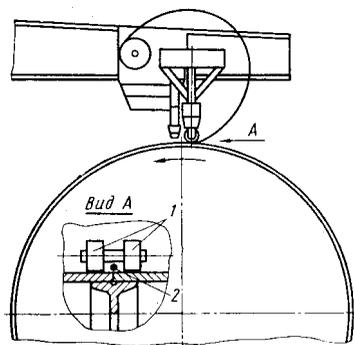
Схема приспособления для прижатия кромок к подкладному кольцу перед сварочной головкой:
